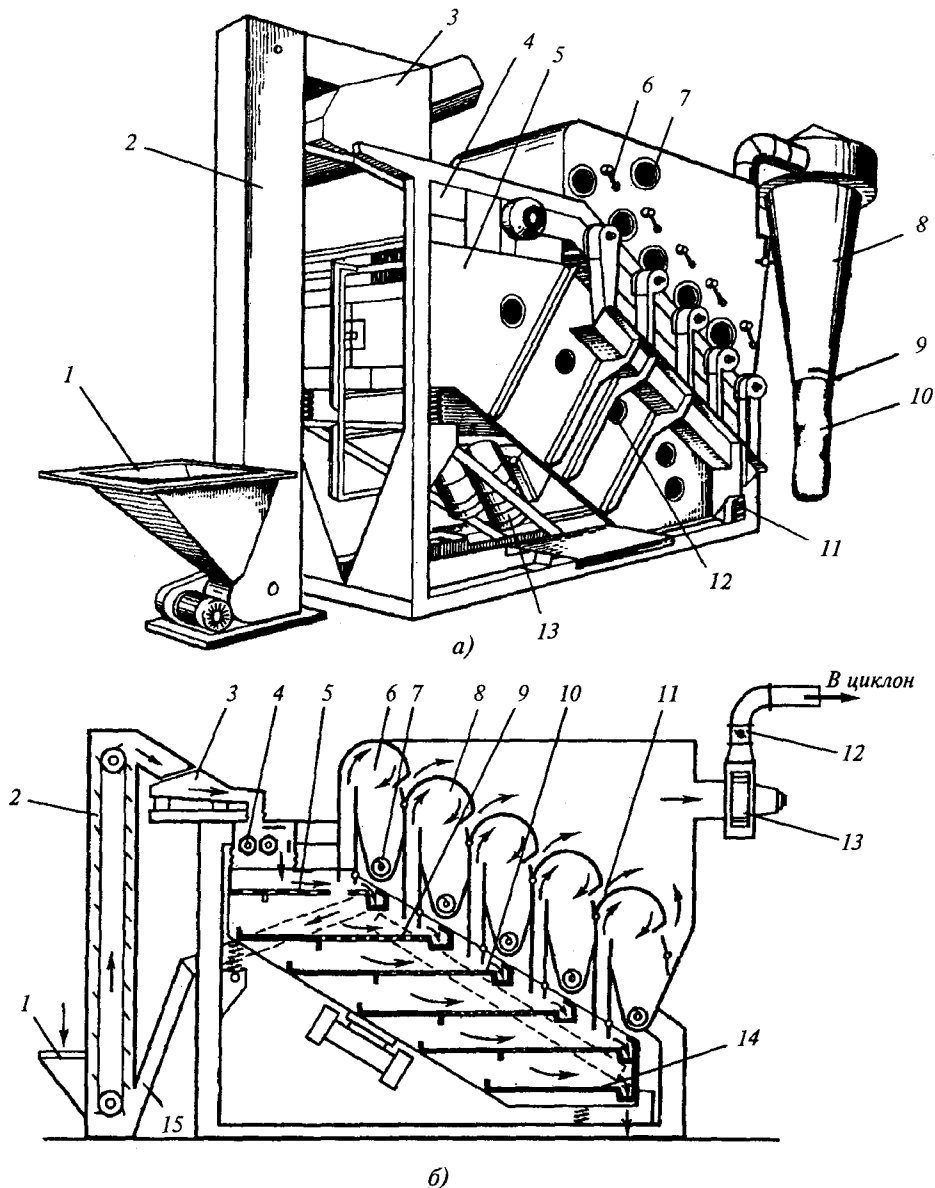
Дробильно-сортировочно-очистительная машина с параллельным расположением сит:
